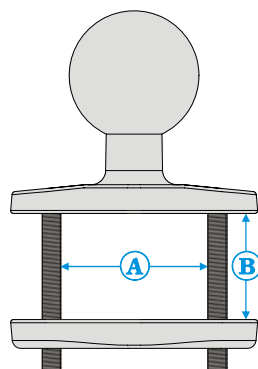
Zusammengesetzte RAM-Klemmhalterung Mounting Dimensions
